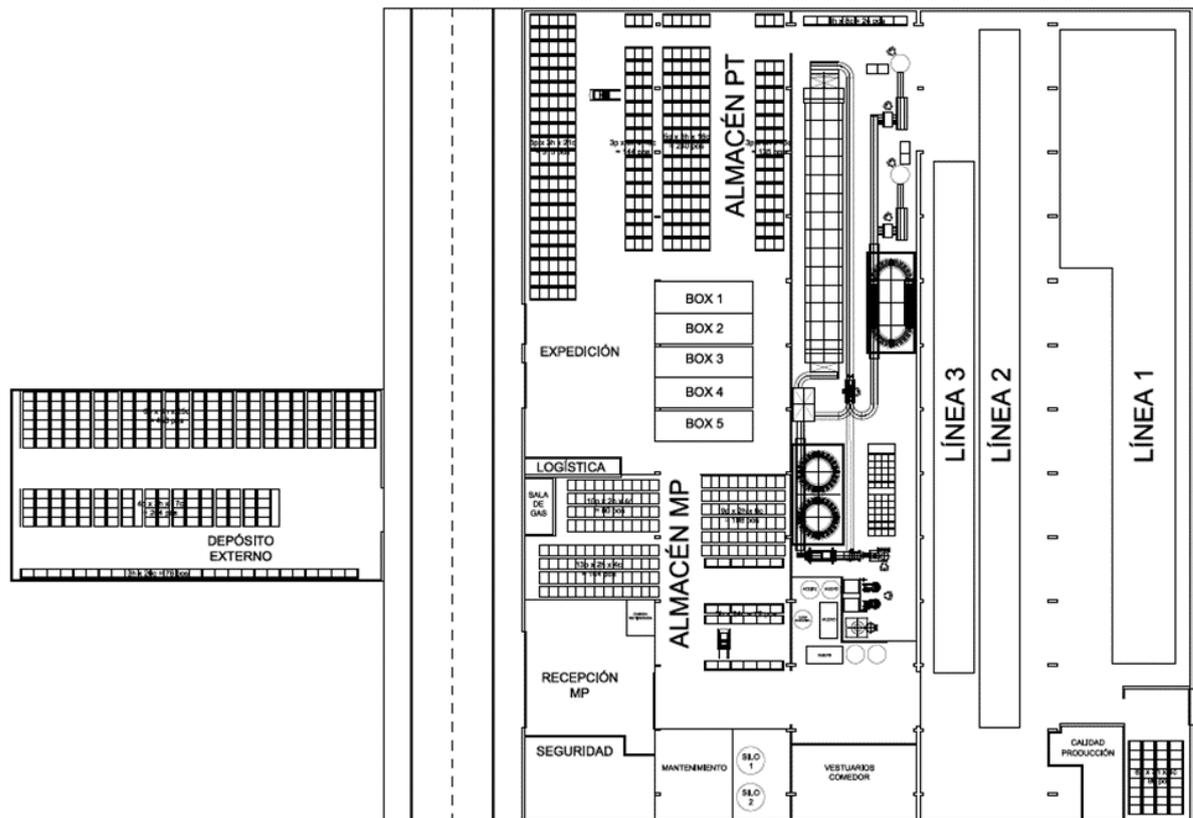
Layout propuesto para la ubicación de la línea de producción en planta. Fuente: Elaboración propia.
